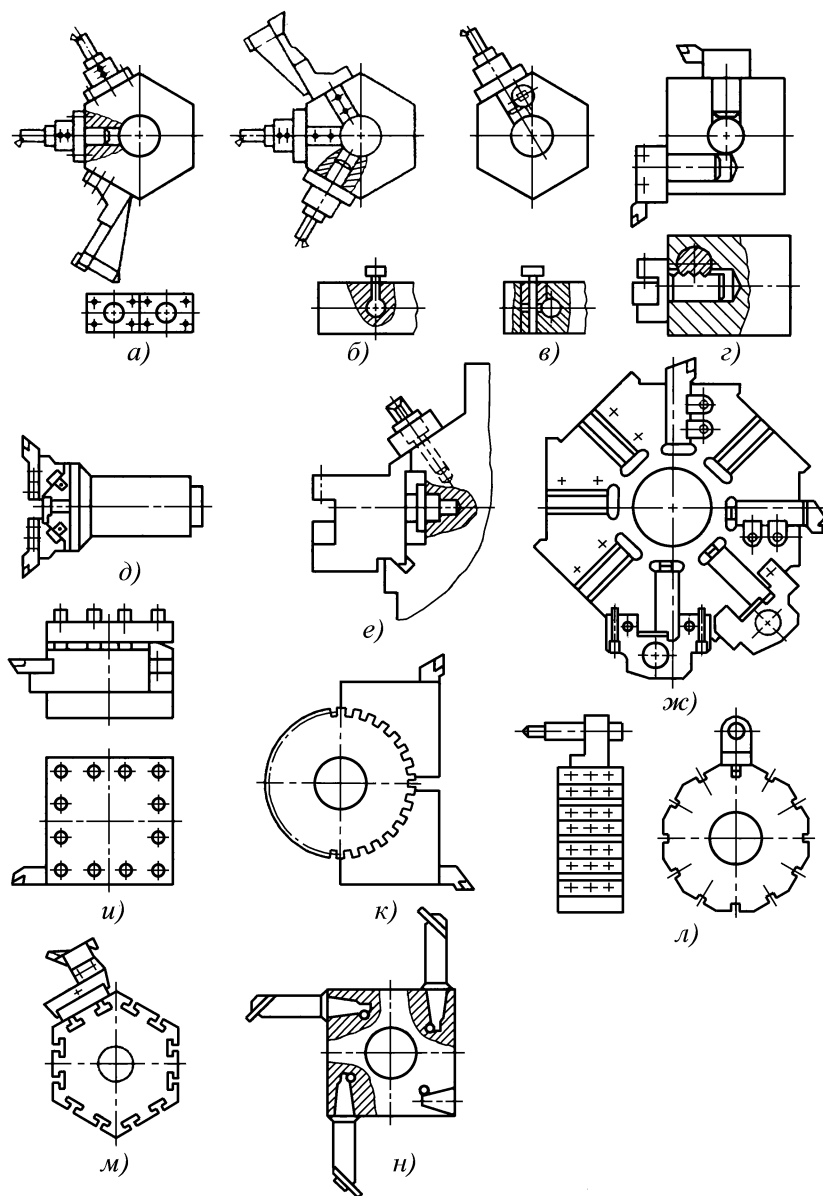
Способы крепления инструмента на токарных станках с ЧПУ
